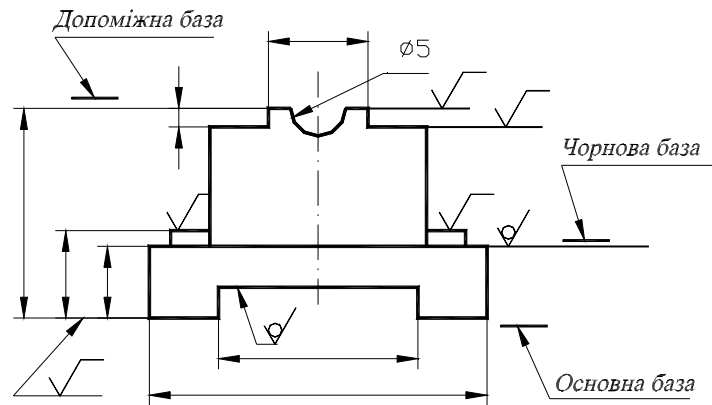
Нанесення розмірів з урахуванням конструкторської бази
